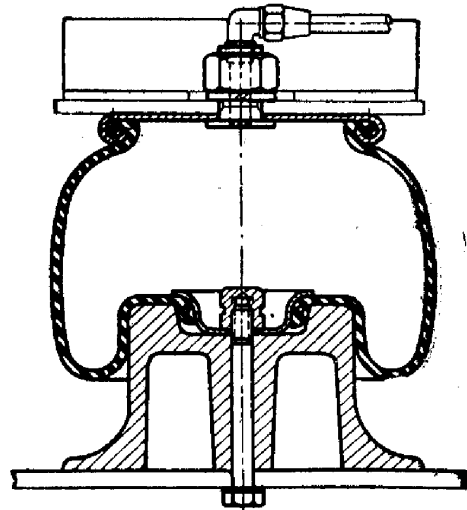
Пневматичний резино-кордний упругий елемент рукавного типу.
